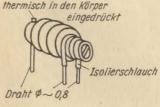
Spulenmontage mit 2 Drahtstücken etwa 0,8 mm Durchmesser
